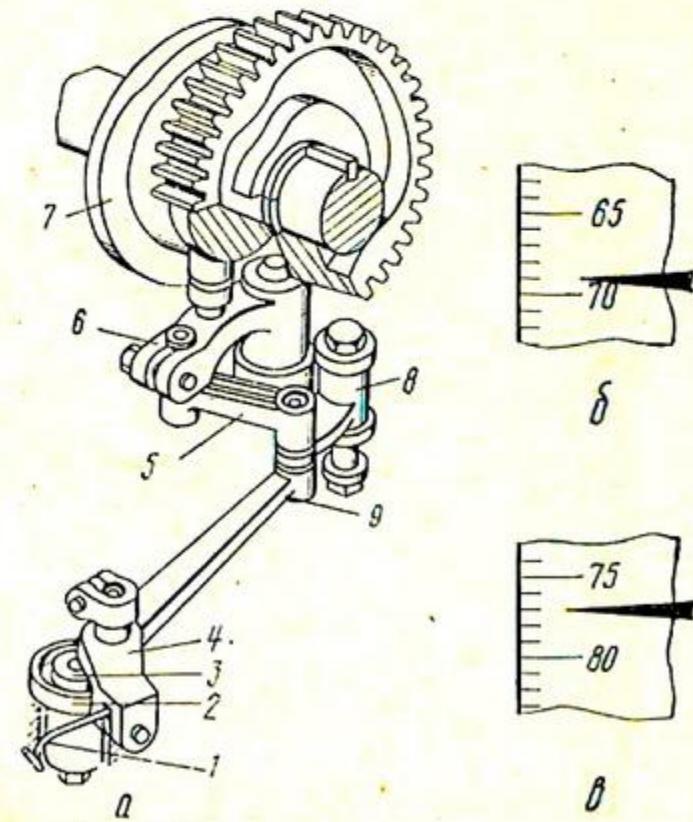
Механизм нитенакидывателя (а) машины СПР и положения главного вала (б, в) при установке нитенакидывателя
